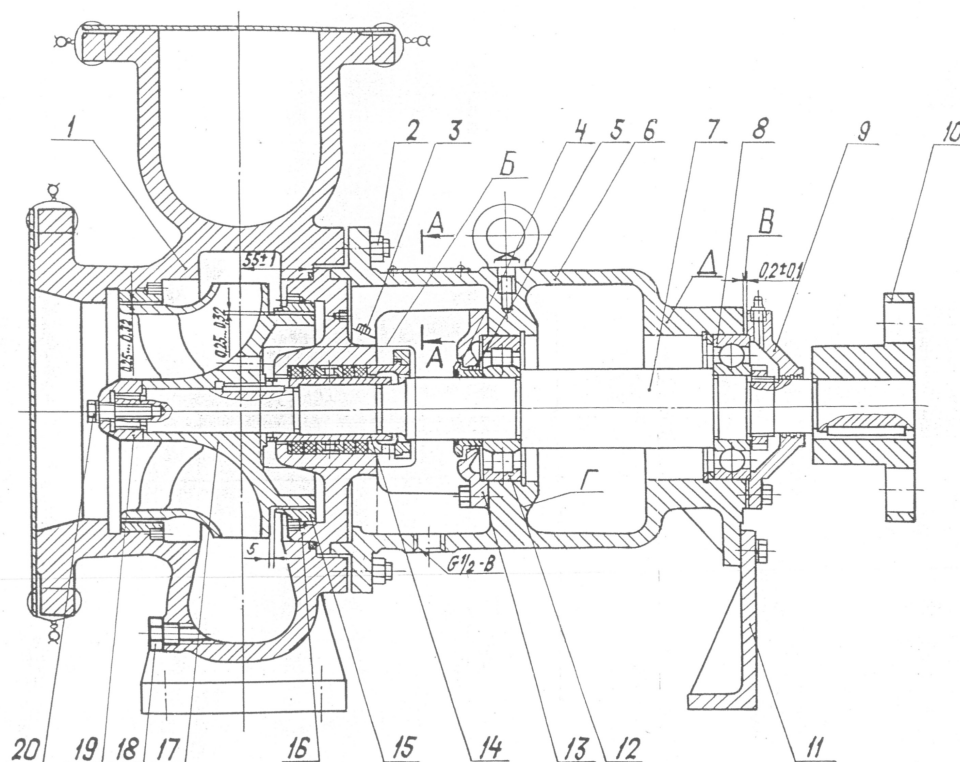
Насос відцентровий типу К: 1- корпус; 2- гайка; 3- пробка 4- кільце; 5- відбійник; 6- кронштейн; 7- вал; 8- підшипник; 9- кришка; 10- напівмуфта насоса; 11- стійка; 12- підшипник; 13- кришка; 14- гільза захисна; 15- кільце щільнине; 16- корпус сальника; 17- колесо робоче; 18- пробка; 19- гайка; 20- болт; 21- кільце; 22- набивка сальника; 23- втулка; 24- фланець натискний; 25- кільце гідрозатвору
